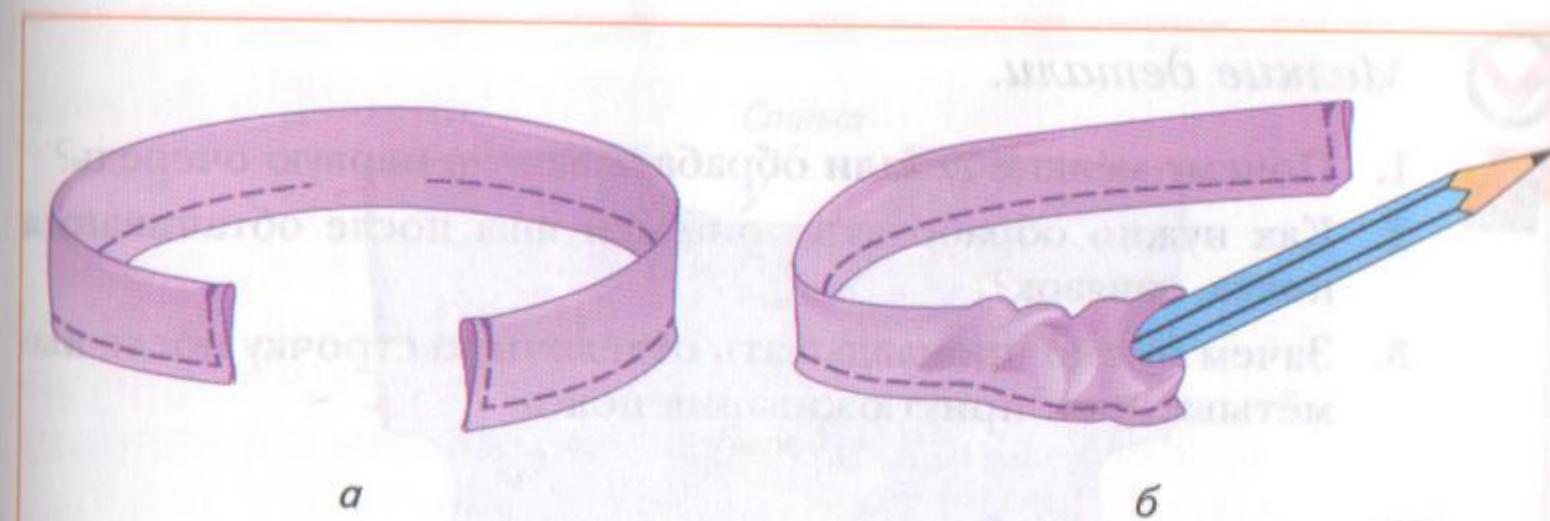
Изготовление мягкого пояса: а — обтачивание; б — вывертывание
